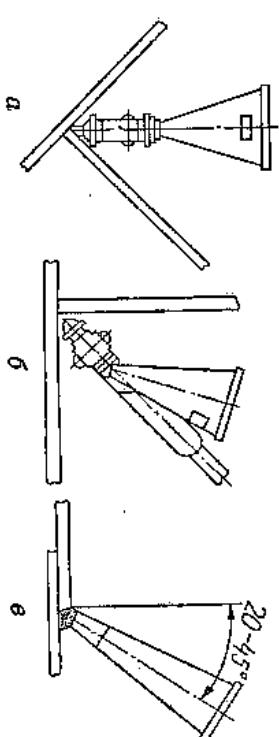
Схемы полуавтоматической сварки под флюсом:
